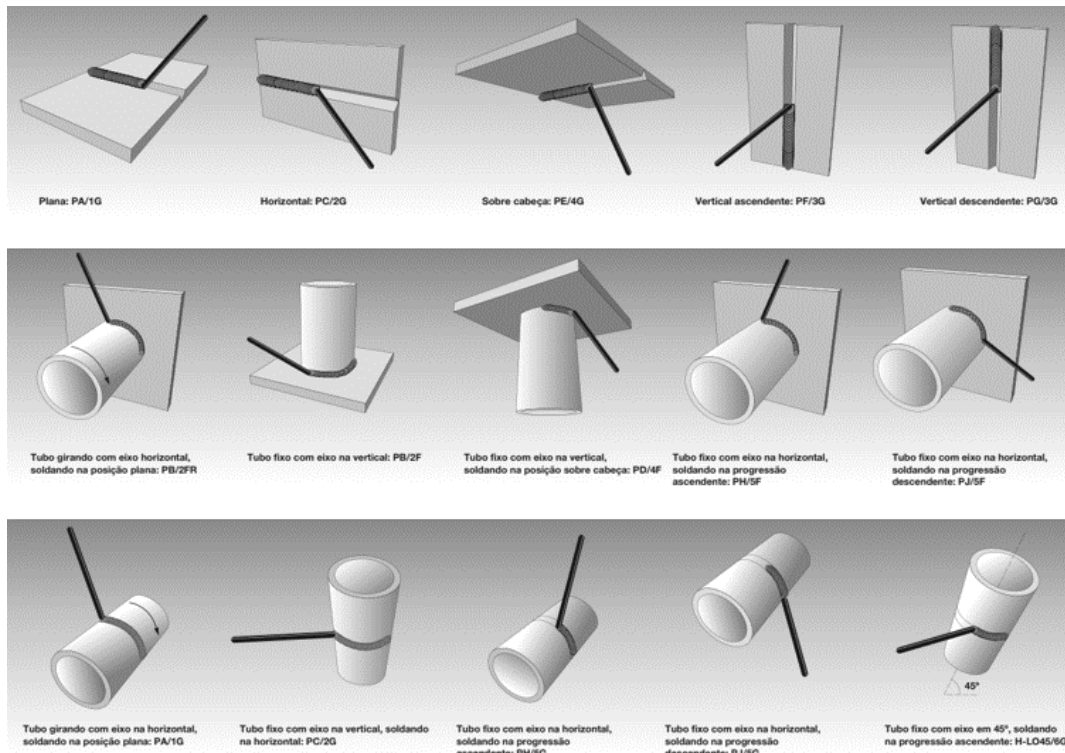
Posições usuais de soldagem (Cartaz: Posições de soldagem ISO e ASME – ESAB)
